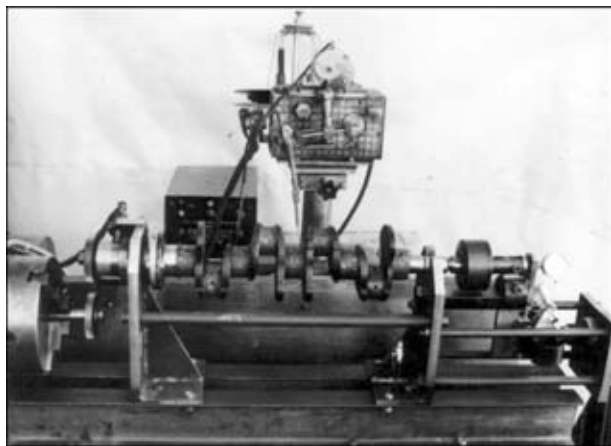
Внешний вид устройства для приложения и регулирования осевого растягивающего усилия к коленчатому валу в процессе наплавки
